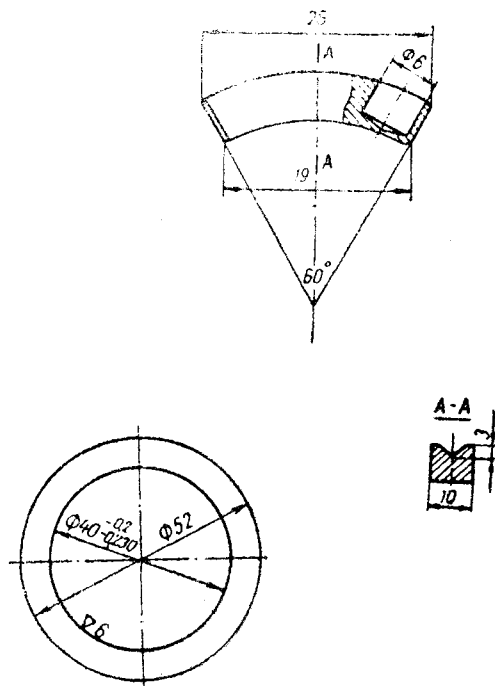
Общий вид буксы: внизу — заготовка, вверху — букса
